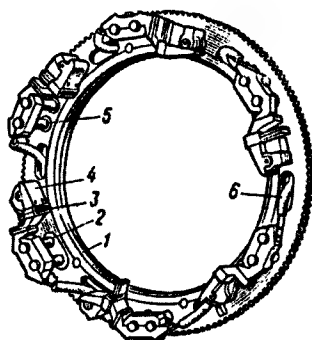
Траверса тяговых двигателей НБ-418К и ТЛ-2К1:
